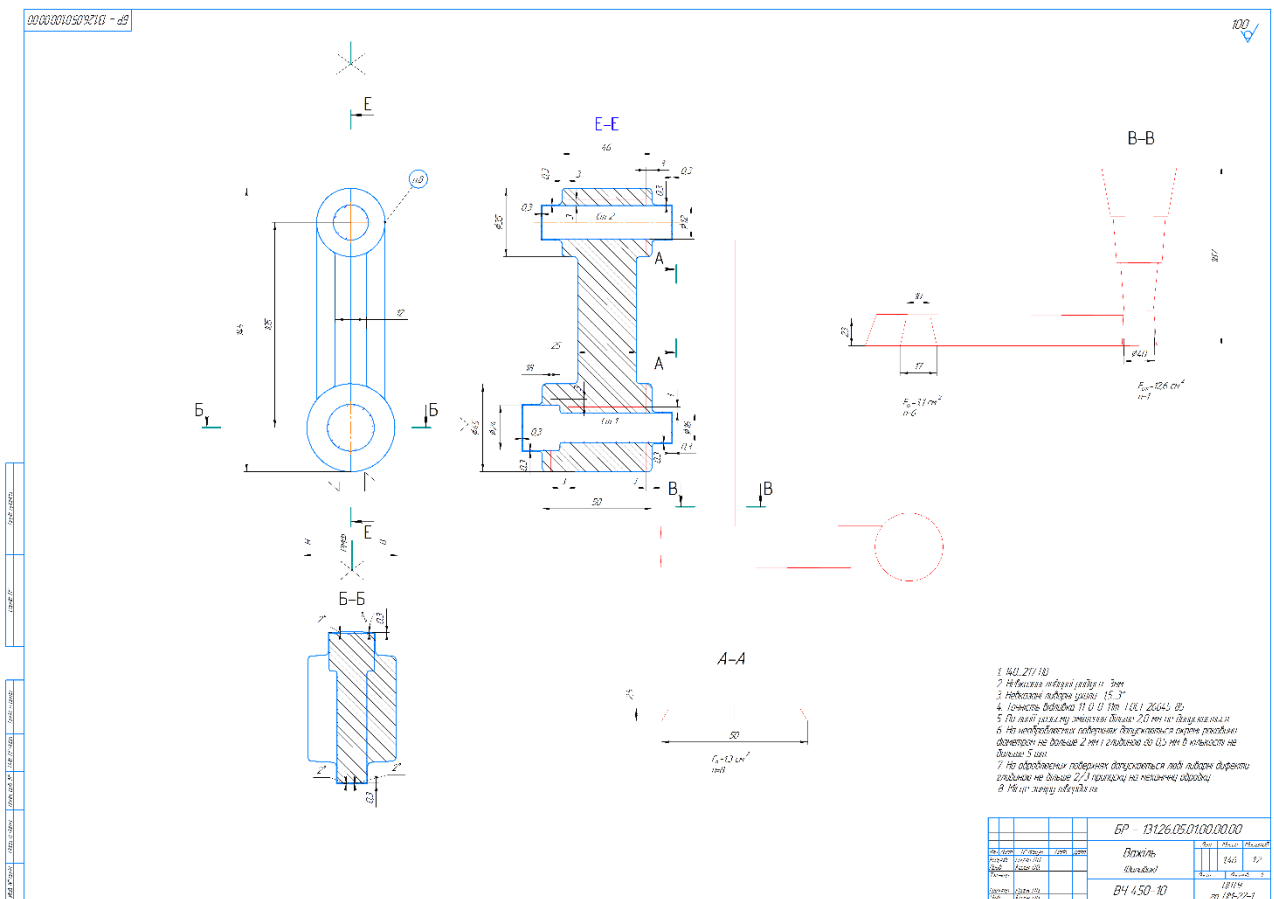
Креслення відливка «Важіль» з модельно-ливарними вказівками
